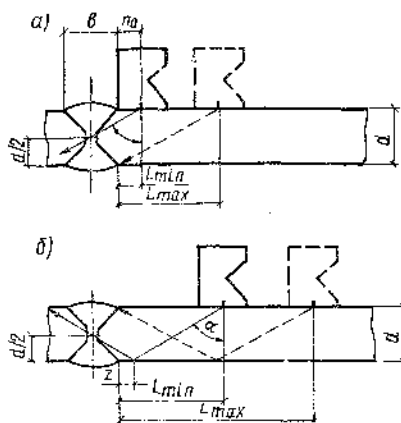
Схемы контроля стыковых сварных соединений
